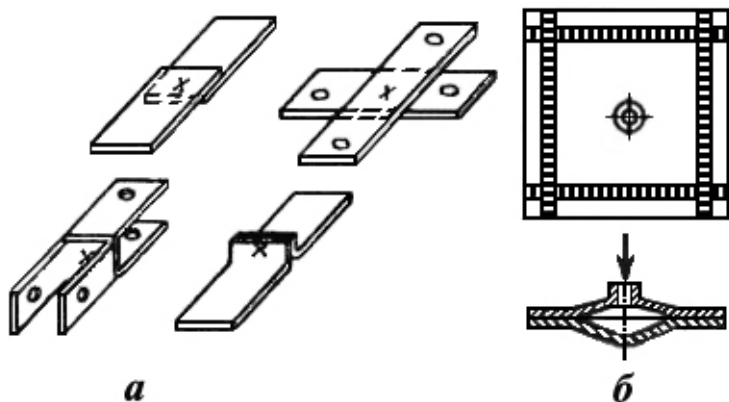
Разновидности образцов для механических испытаний: а — образцы для испытаний на разрывной машине; б — образец для гидроиспытаний на прочность и герметичность соединений, полученных шовной сваркой
